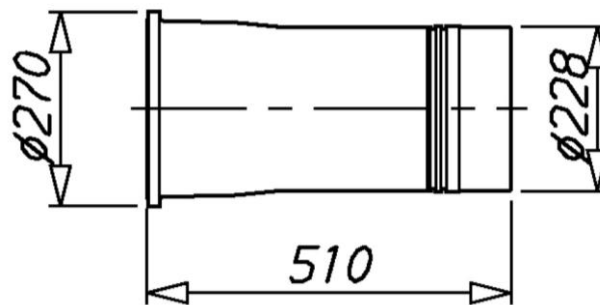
Втулка робочого циліндра двигуна 4ЧН 20/28
